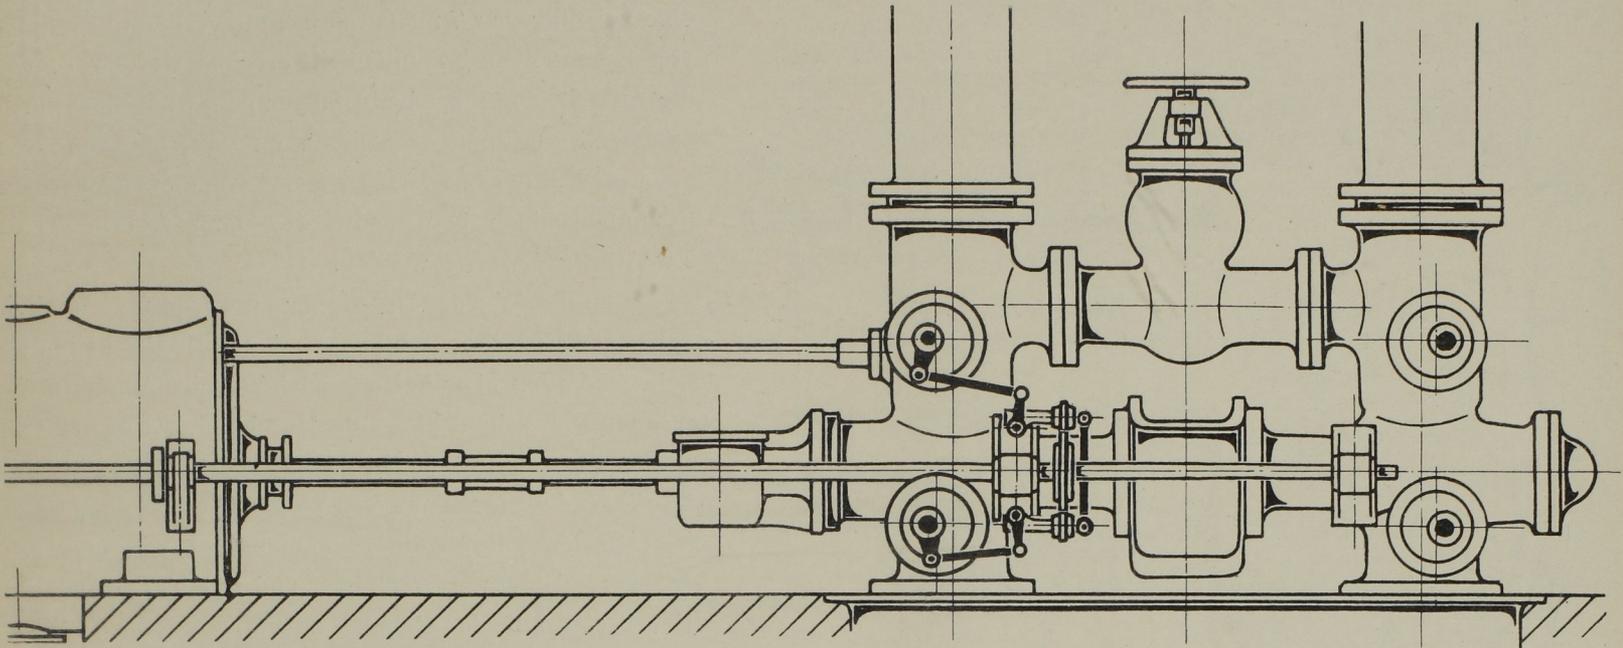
Seitenansicht der Druckpumpe. Masst. 1:30.
